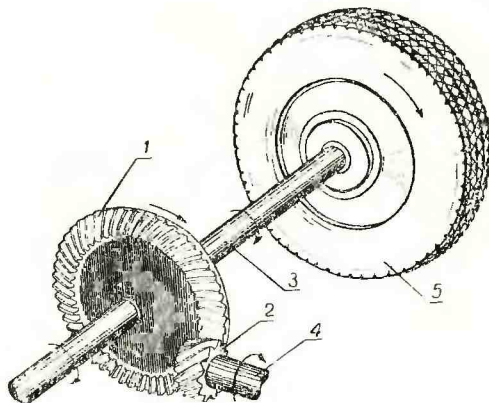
Принцип конструкции главной передачи: 1 — коронная шестерня; 2 — ведущая шестерня; 3 — задняя ось; 4 — ведущий вал; 5 — заднее колесо автомобиля
